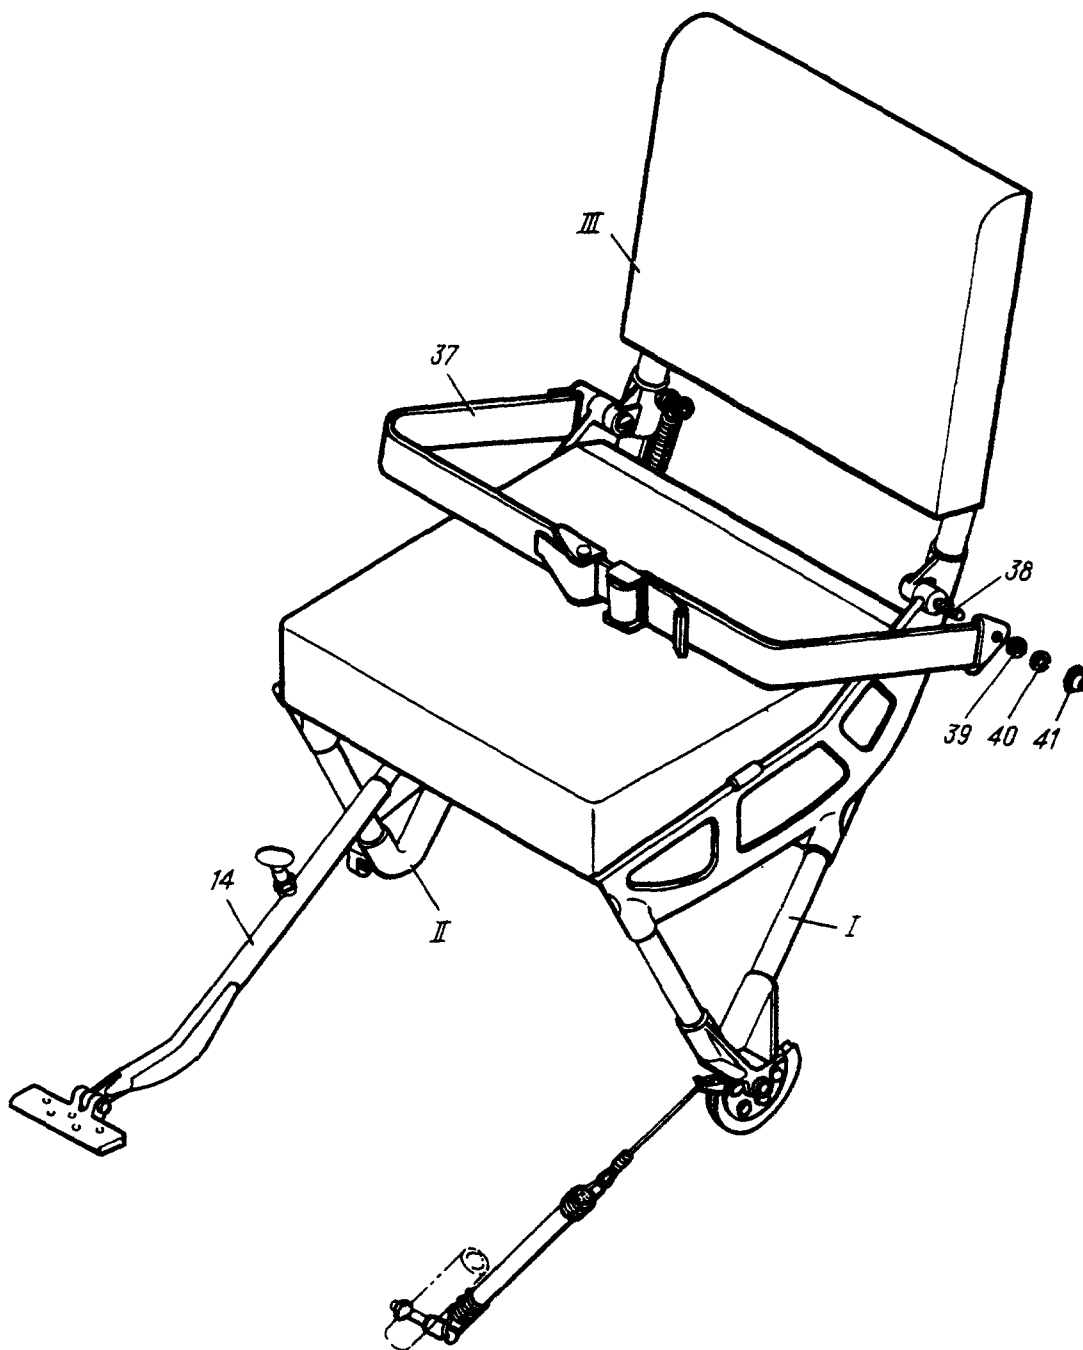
КРЕСЛО БОРТТЕХНИКА (Лист I из 5)
